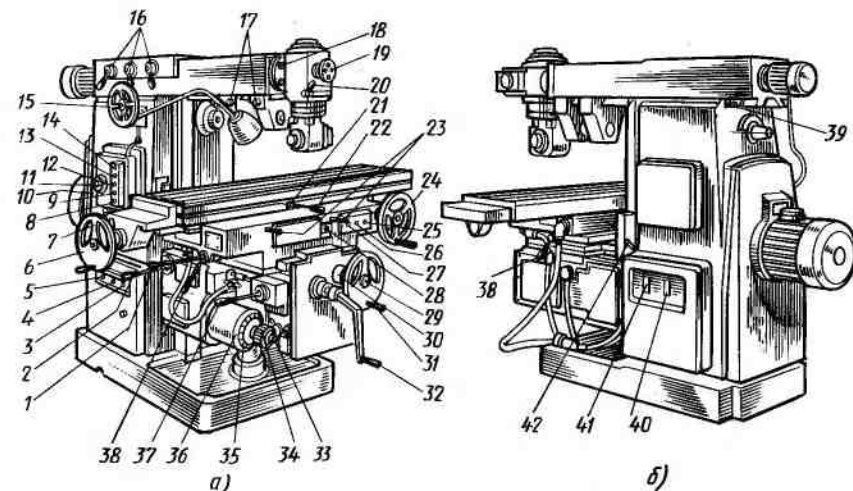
Общий вид станка мод. 6P82Ш:
